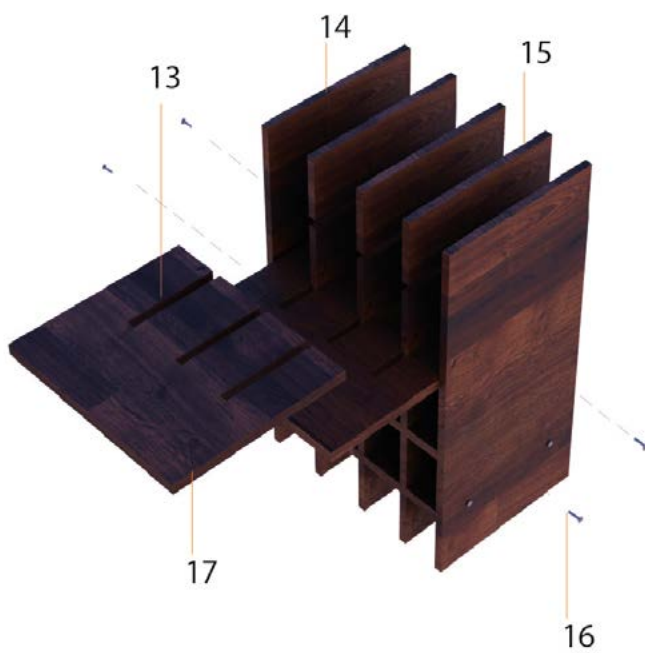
Detalle constructivo 3d vinera con madera MDF
